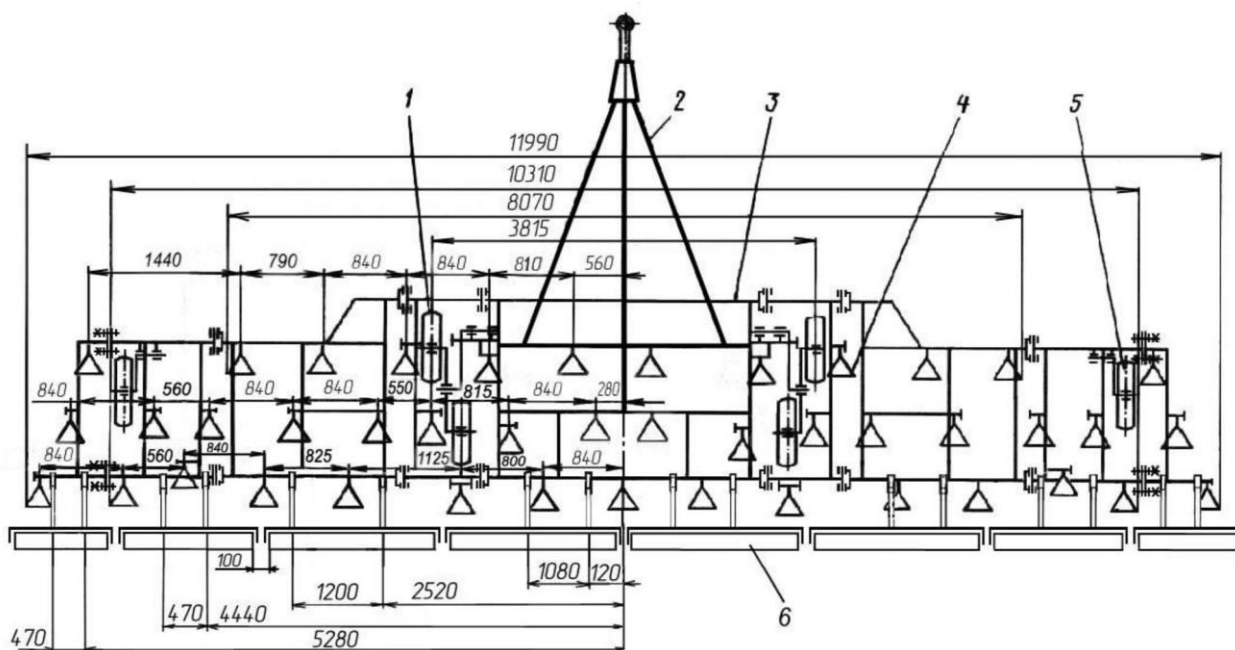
Схема расстановки рабочих органов модернизированного культиватора КШУ-12: 1 – механизм подката; 2 – спица; 3 – рама; 4 – подвеска; 5 – колесо; 6 – борона роторная
